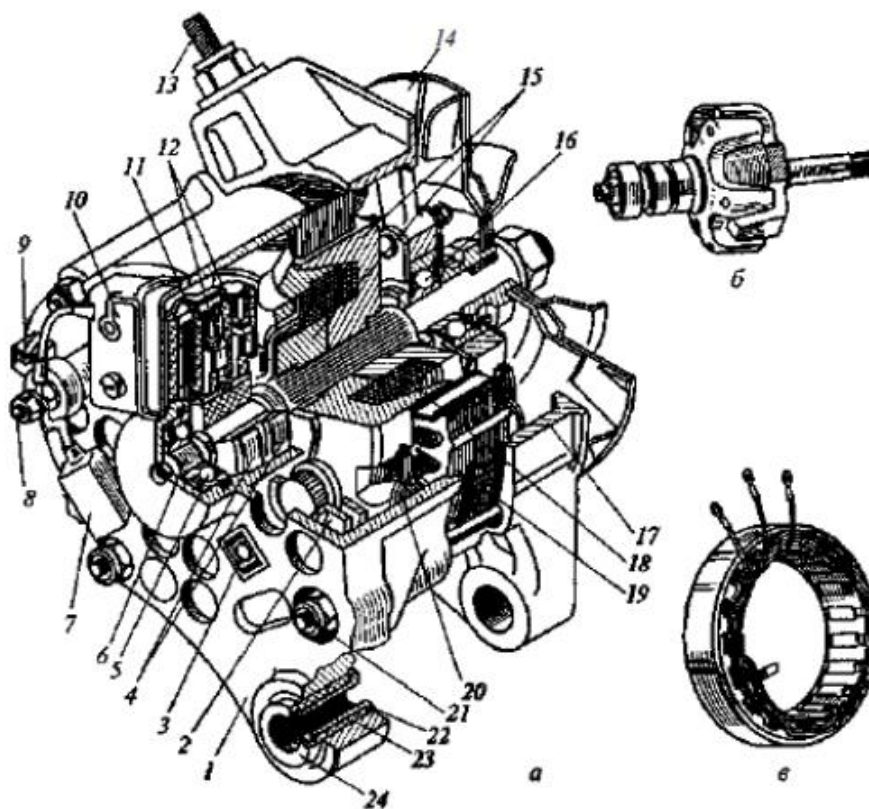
Генератор Г-222: а – общий вид; б – полюсные наконечники ротора; в – статор с обмоткой; 1 – крышка; 2 – блок выпрямителей; 3 – винт; 4 – контактные кольца; 5 и 16 – подшипники; б – вал; 7 – чехол вывода;
